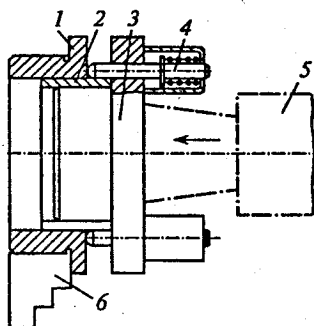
Схема установки свертной втулки в отверстие детали на токарном станке:
